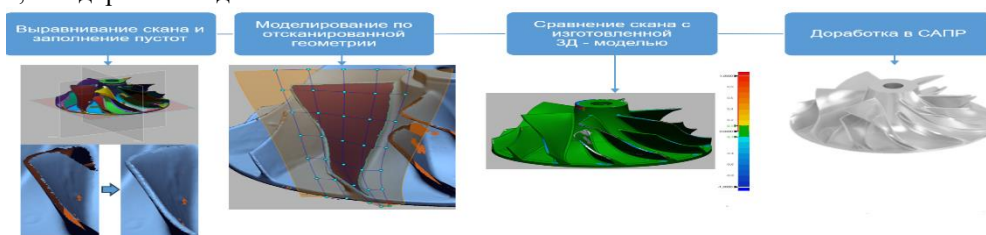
Процесс создания 3Д - модели детали “колесо компрессора”
